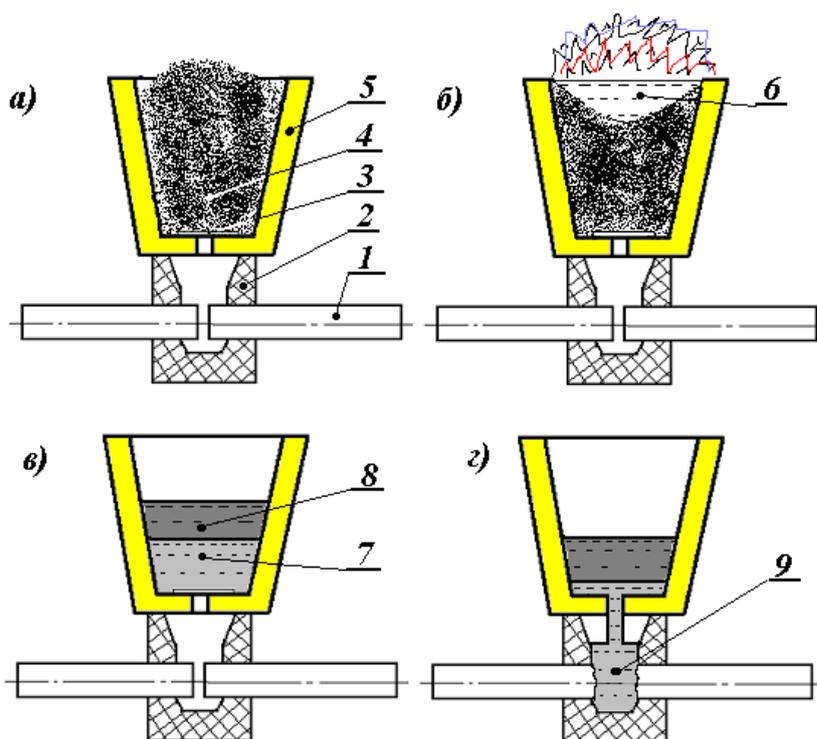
Стадии процесса термитной сварки плавлением
